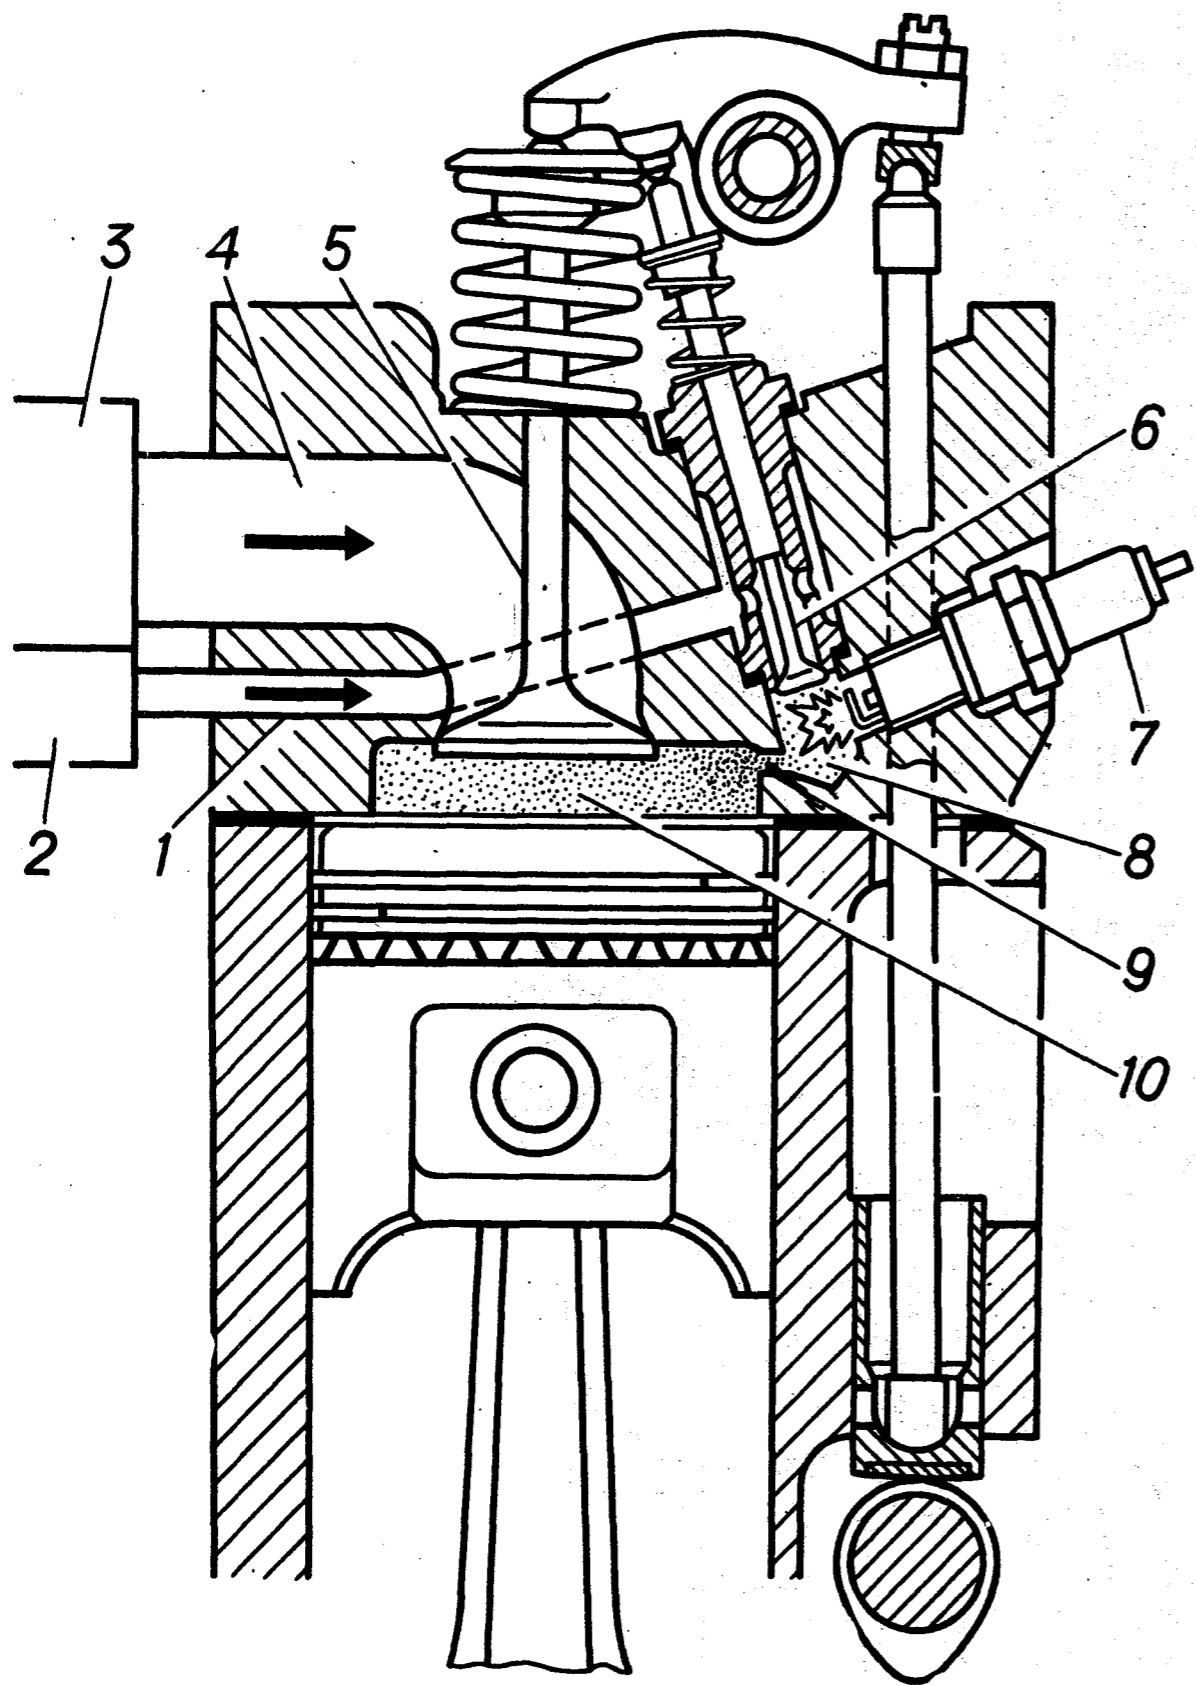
Схема двигателя с форкамерно-факельным зажиганием:
